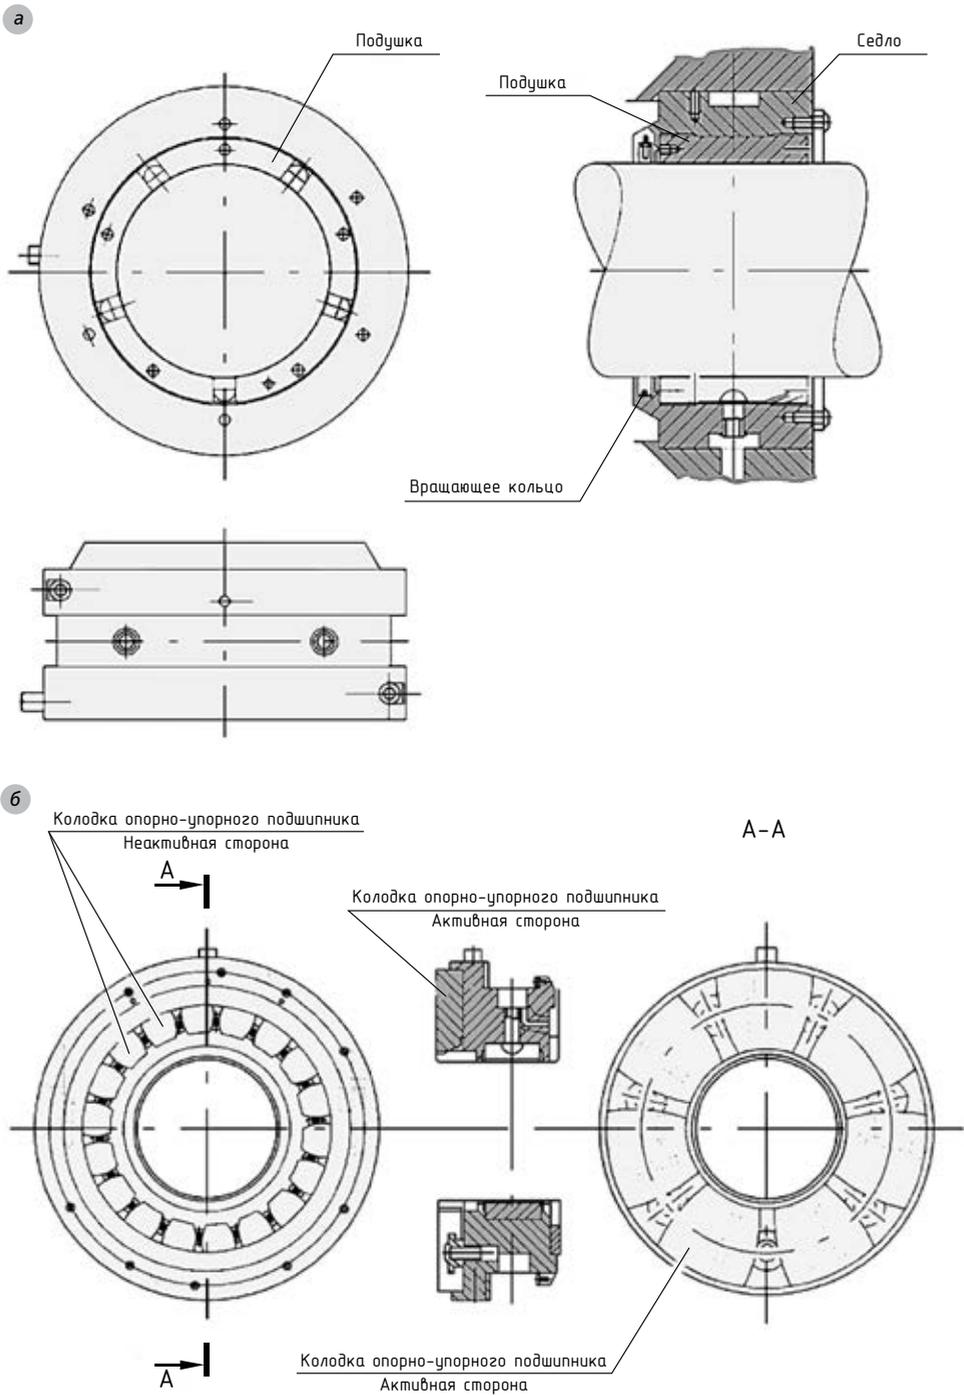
Подшипники ТНД: а) опорный подшипник № 3;
